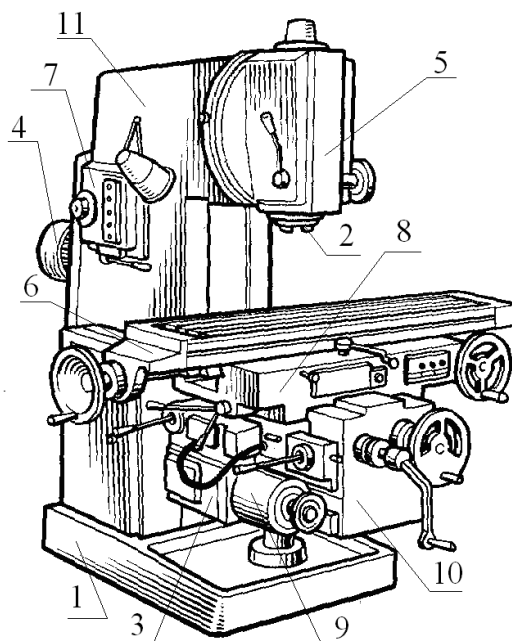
Загальний вигляд вертикально-фрезерного верстата:
